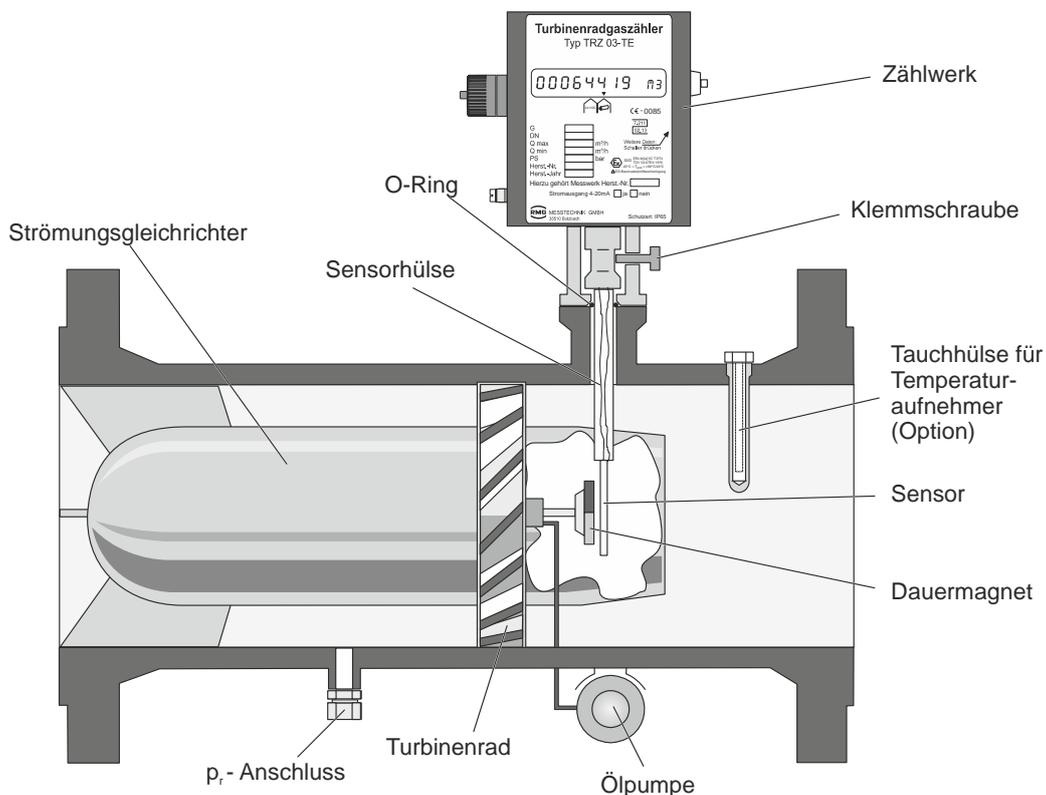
Schnittzeichnung Turbinenradgaszähler
